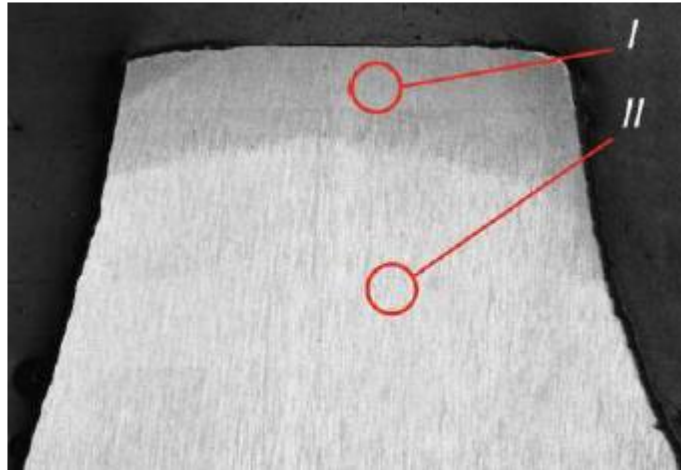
Фотографія нової пилки з високим зубом;
